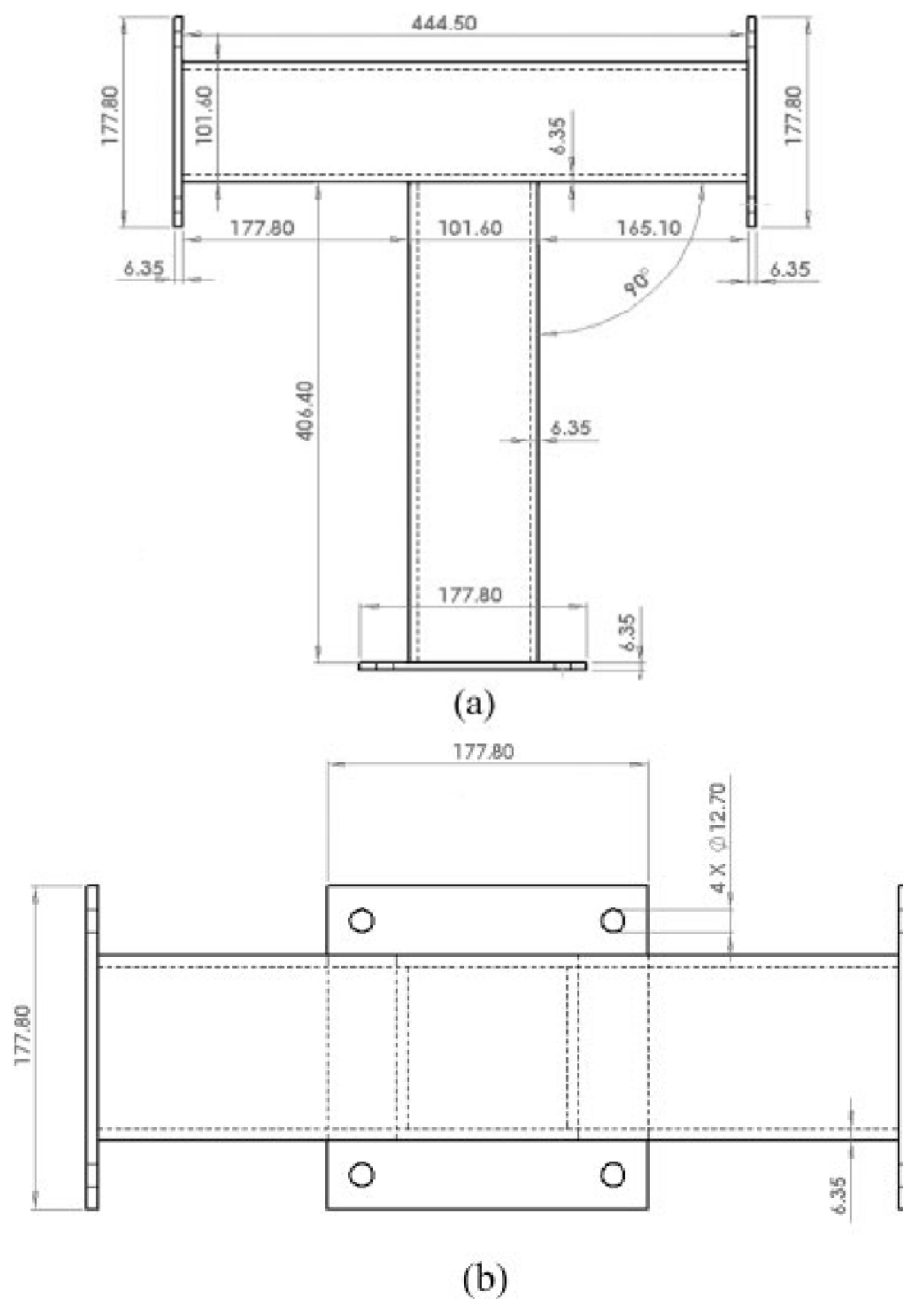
Configuración y dimensiones de la unión en T: (a) vista frontal; (b) vista superior [31]
